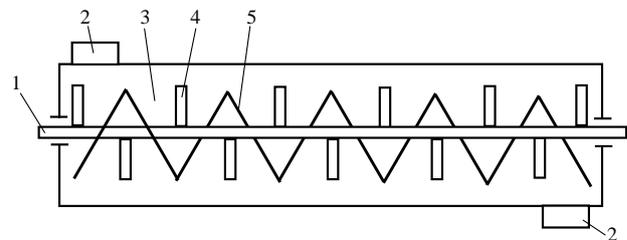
Предлагаемая схема конструкции смесителя-измельчителя: 1 – вал; 2 – загрузочные и выходные отверстия; 3 – корпус; 4 – измельчающие рабочие органы; 5 – смешивающие рабочие органы
